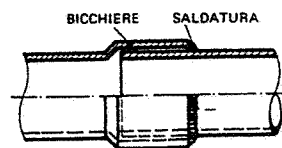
Giunto a bicchiere cilindrico saldato.
